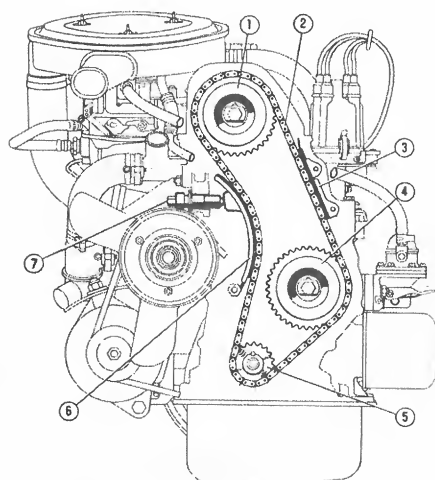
Цепной привод распределительного вала: 1 — ведомая звездочка распределительного вала; 2 — цепь; 3 — успокоитель; 4 — ведомая звездочка промежуточного вала; 5 — ведущая звездочка; 6 — натяжное устройство; 7 — плунжер.
